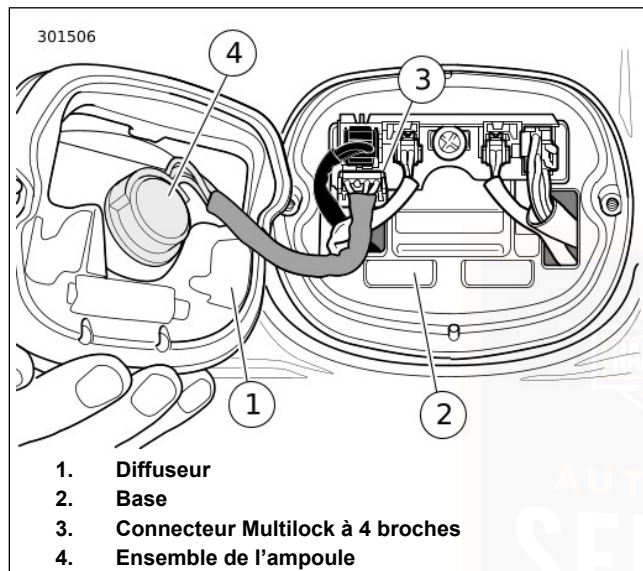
Ensemble du feu arrière : FLSTC/FLSTF
